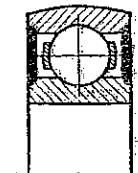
Шарикоподшипник со сферической поверхностью наружного кольца
